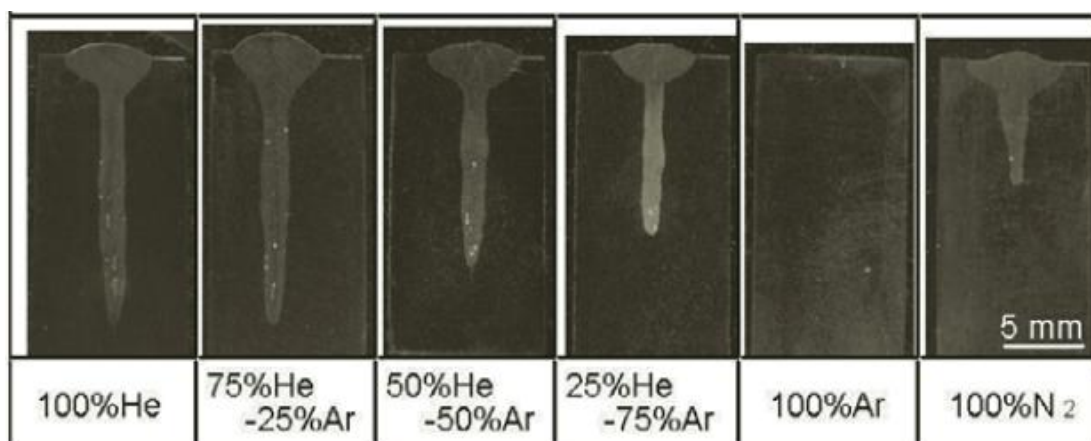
Geometrias de cordão para diferentes gases de soldagem. (11)
